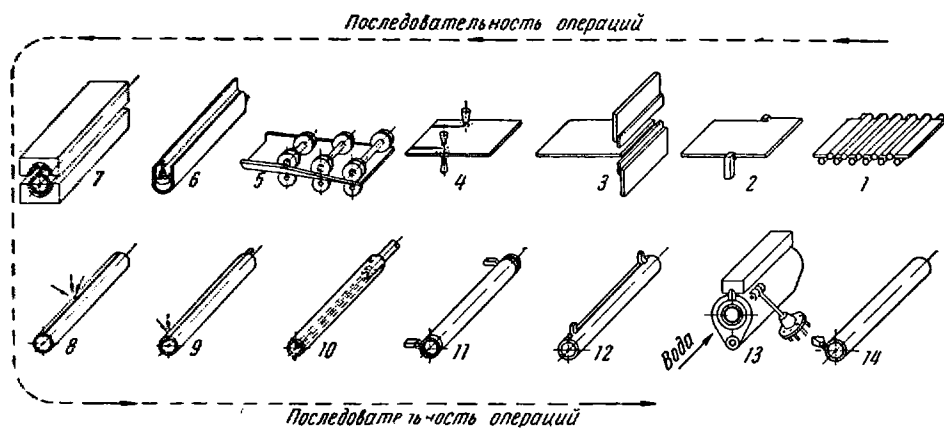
Схема технологического процесса производства сварных труб под слоем флюса:
